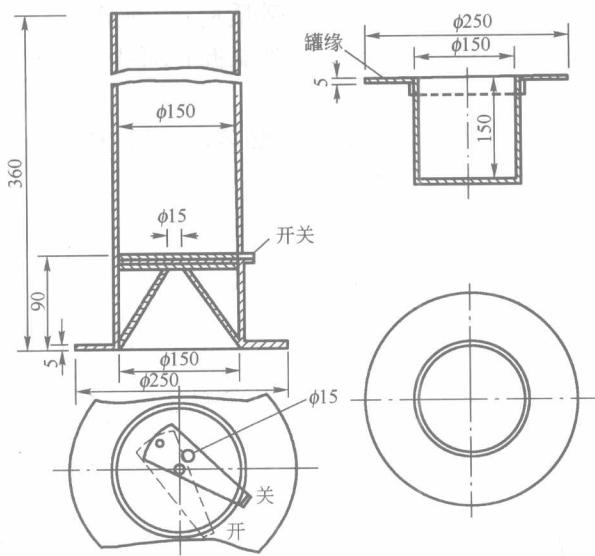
灌砂筒和标定罐(尺寸单位:mm)
